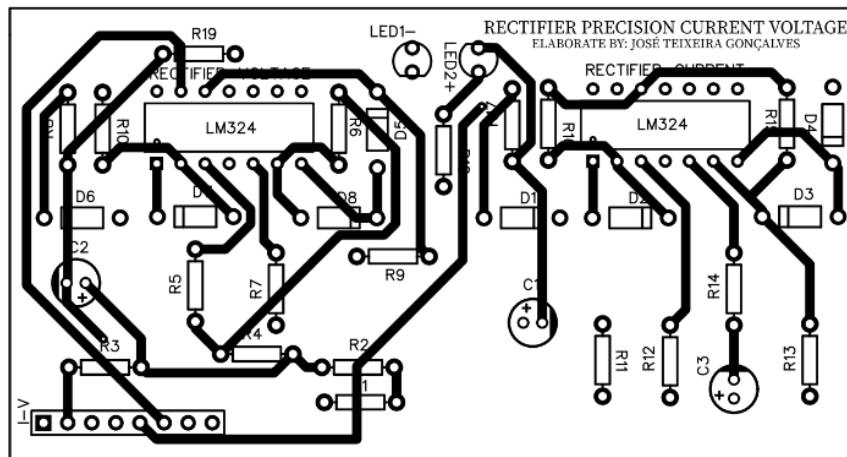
Placa PCB da camada inferior do retificador de precisão.
